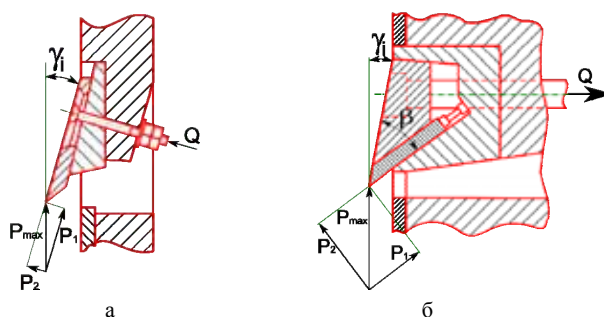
Схемы для расчета крепления ножей на диске: а – нож с лицевой стороны; б – нож в повернутом положении
